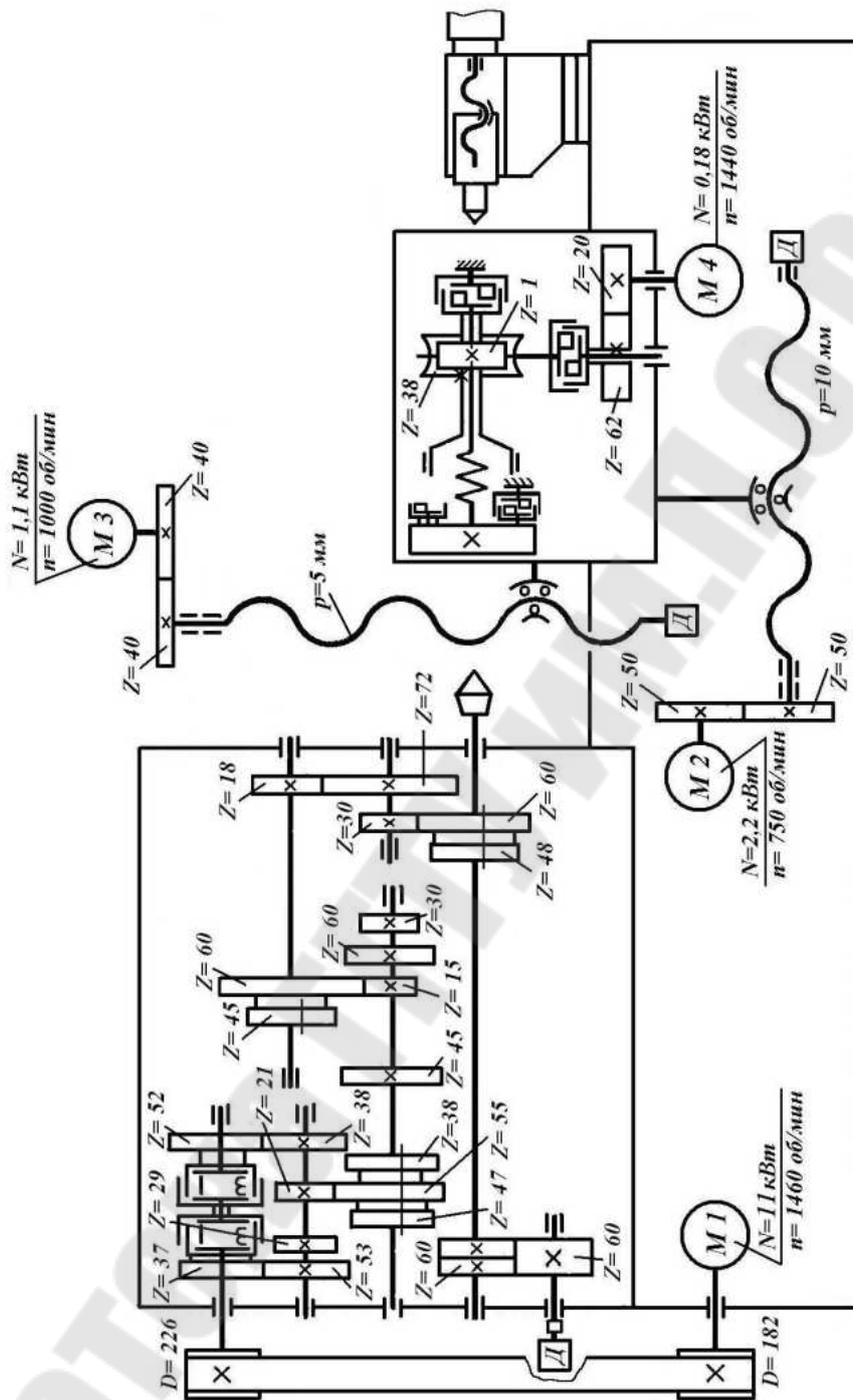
Кинематическая схема токарно-винторезного станка с ЧПУ 16К20Г1
